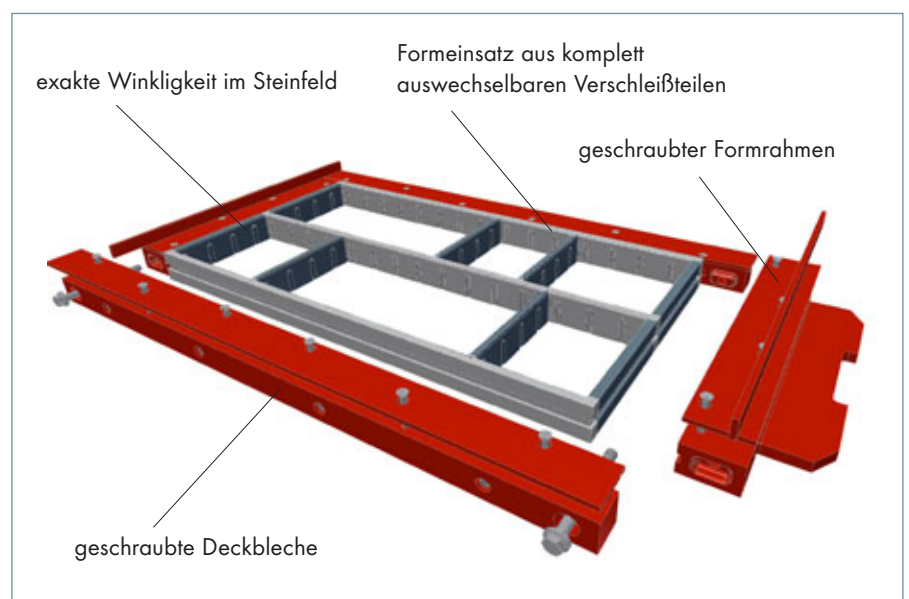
Modulare Bauweise einer Kobra-Betonsteinform
